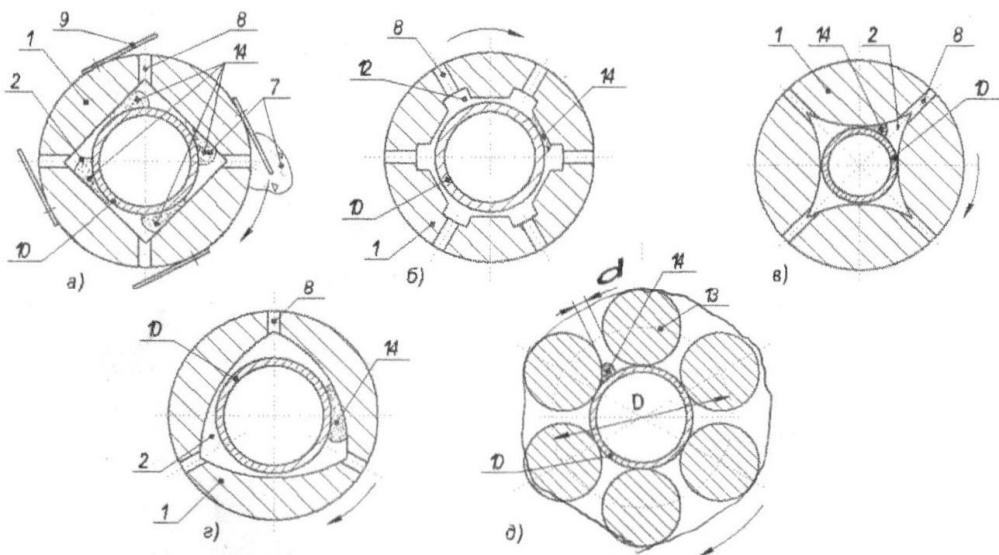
Форми поперечного перетину робочої зони установки (рис.1 – збільшено).
